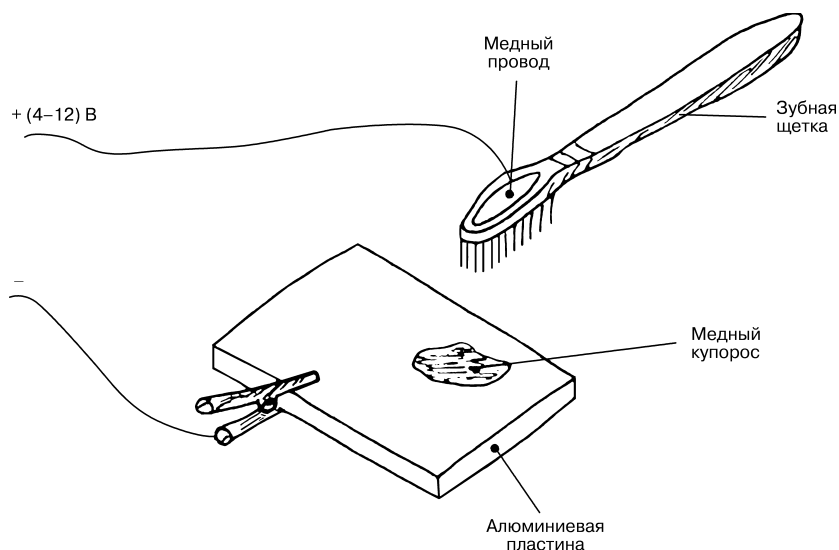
Устройство для омеднения алюминиевой поверхности
